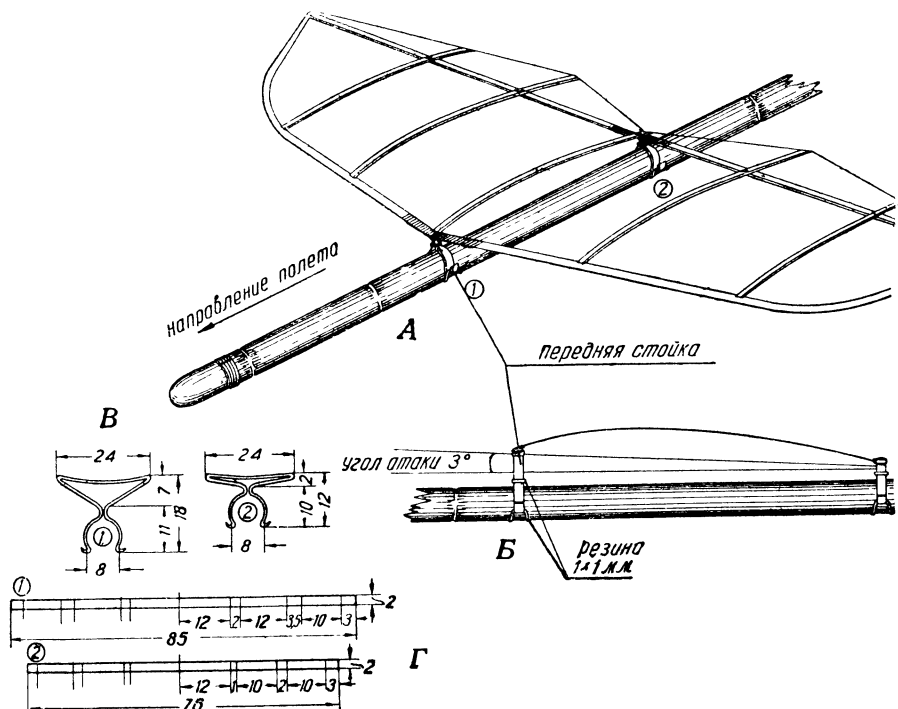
Крепление стабилизатора: А — общий вид крепления; Б — вид крепления сбоку; В — передняя и задняя стойки крепления стабилизатора; Г — рабочие развертки стоек
